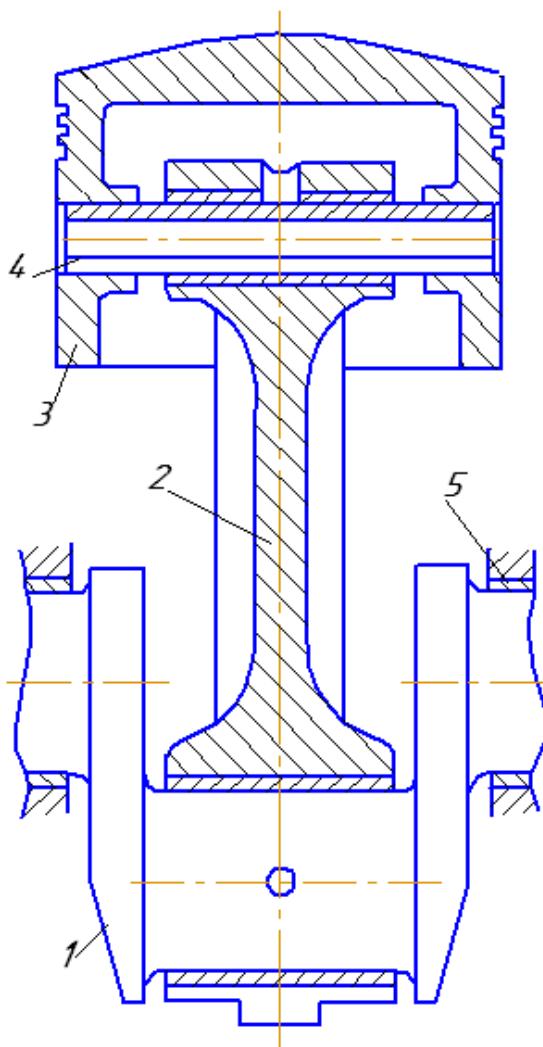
Кривошипно-поршневой узел двигателя
